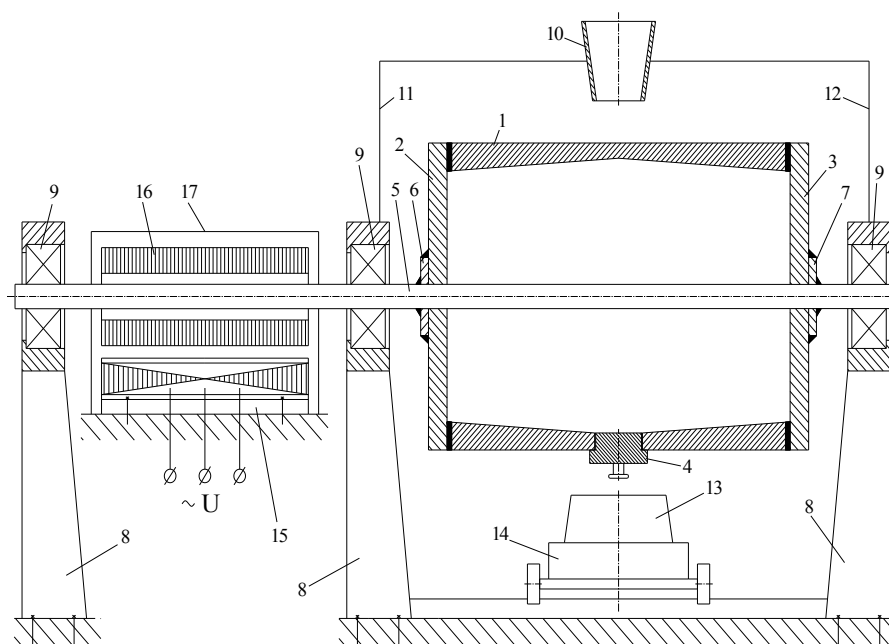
Установка для смешивания порошковых материалов с бесступенчатым приводом
